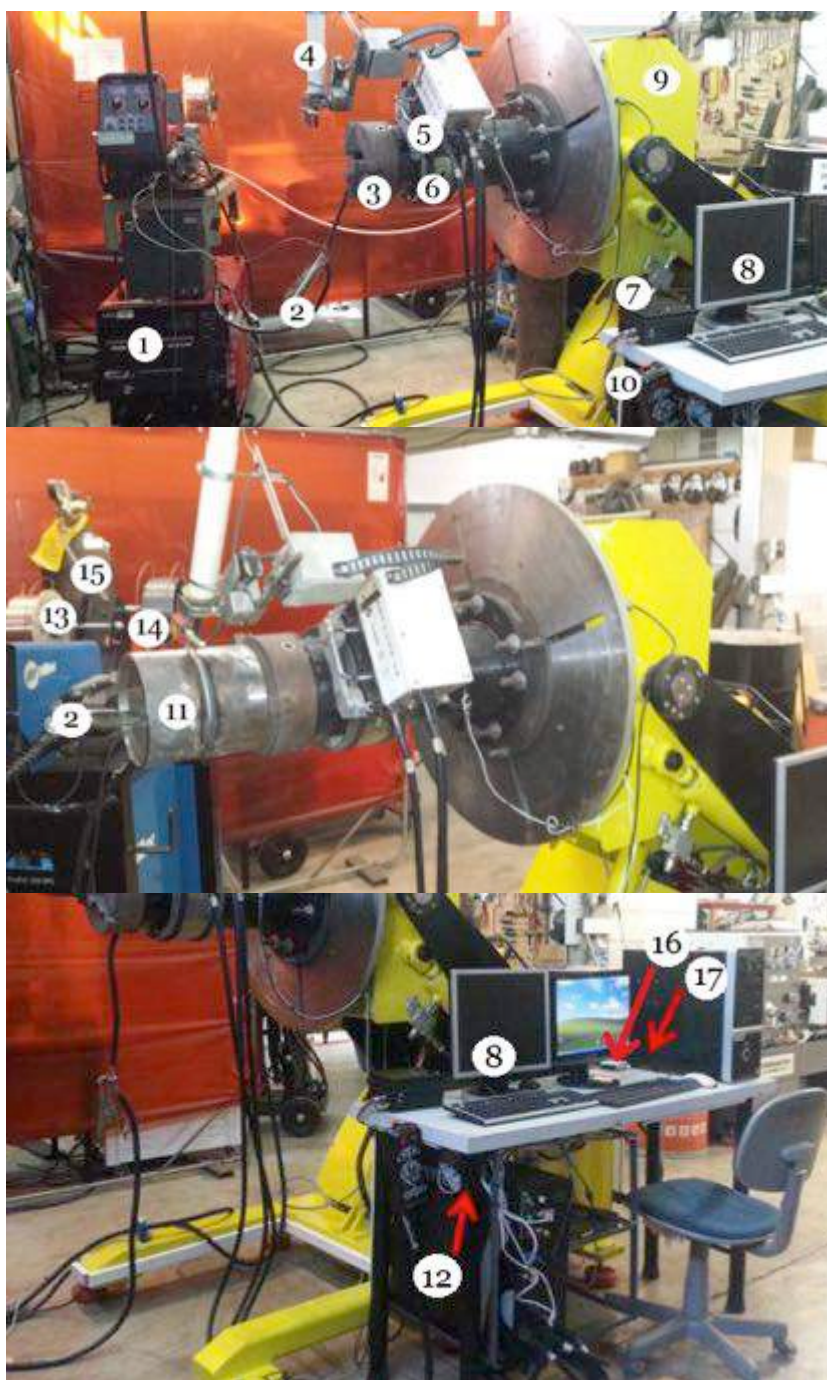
Bancada experimental utilizada, sendo 1. Fonte de soldagem; 2. Cabo terra da fonte de soldagem (aterramento em ambos os lados do tubo); 3. Suporte do tubo teste ("castanha"); 4. Tocha de soldagem; 5. Carrinho de movimentação da tocha (Tartilope V4); 6. Cinta de suporte para movimentação angular do carrinho. 7. Sistema de controle de ajuste automático da DBCP; 8. Monitor de visualização dos parâmetros de movimentação da tocha; 9. Mesa posicionadora; 10. Controle manual de manipulação da tocha; 11. Tubo teste; 12. Sistema de controle do manipulador da tocha (Tartilope); 13. Arame ER70S-6 com 1,2 mm de diâmetro; 14. Sensor *laser*; 15. Cilindro de gás; 16. Placa de aquisição (National Instruments modelo NI USB-6009); 17. Sistema de aquisição de dados
